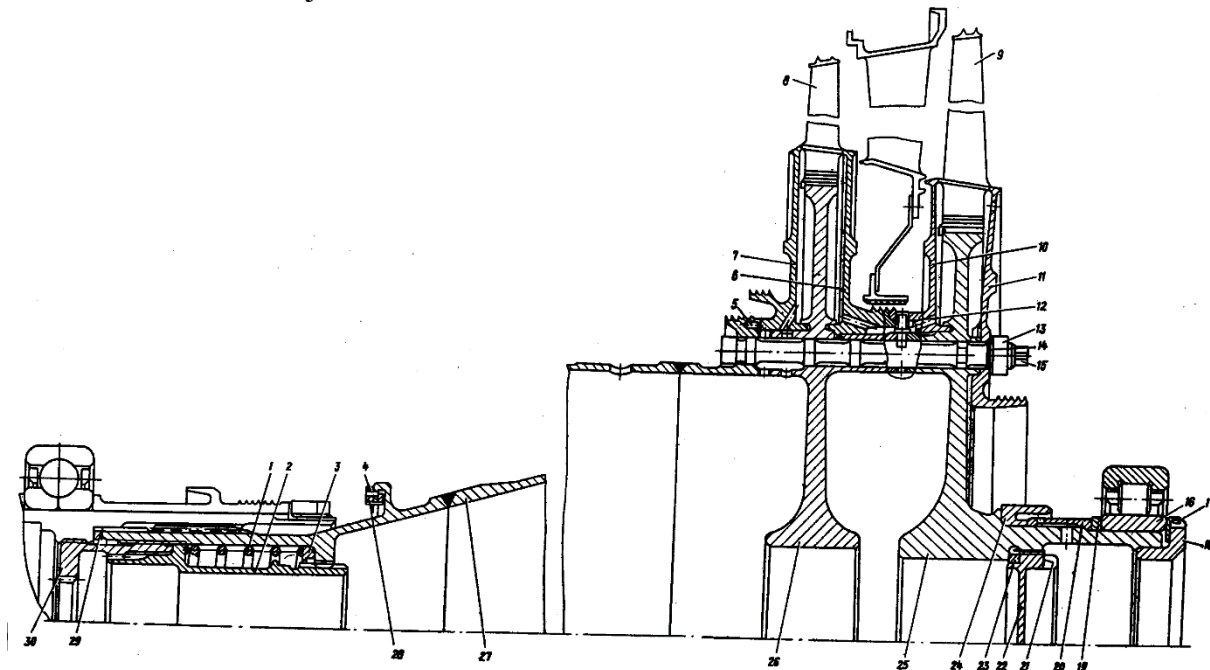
Podélný řez státorem plynové turbíny kompresoru
